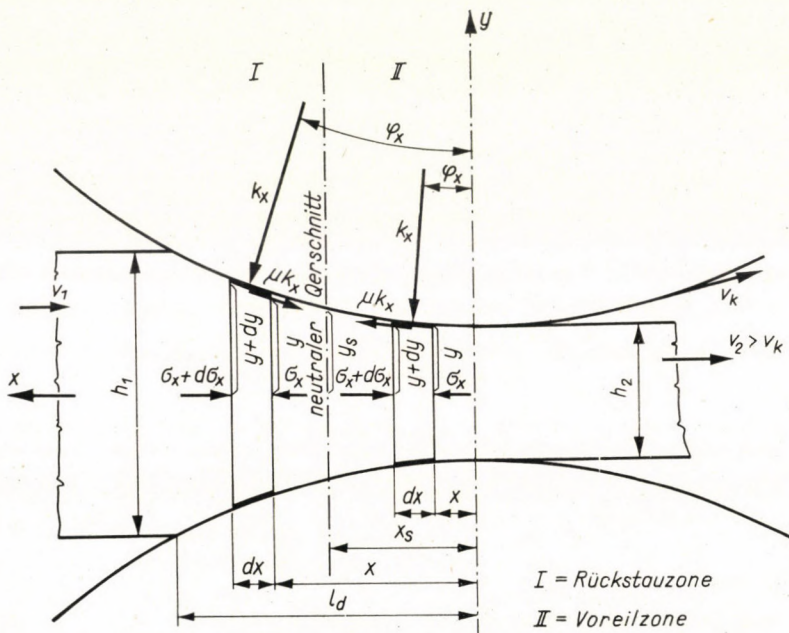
Am Volumenelement des Walzstabes angreifende Kräfte im Walzspalt
